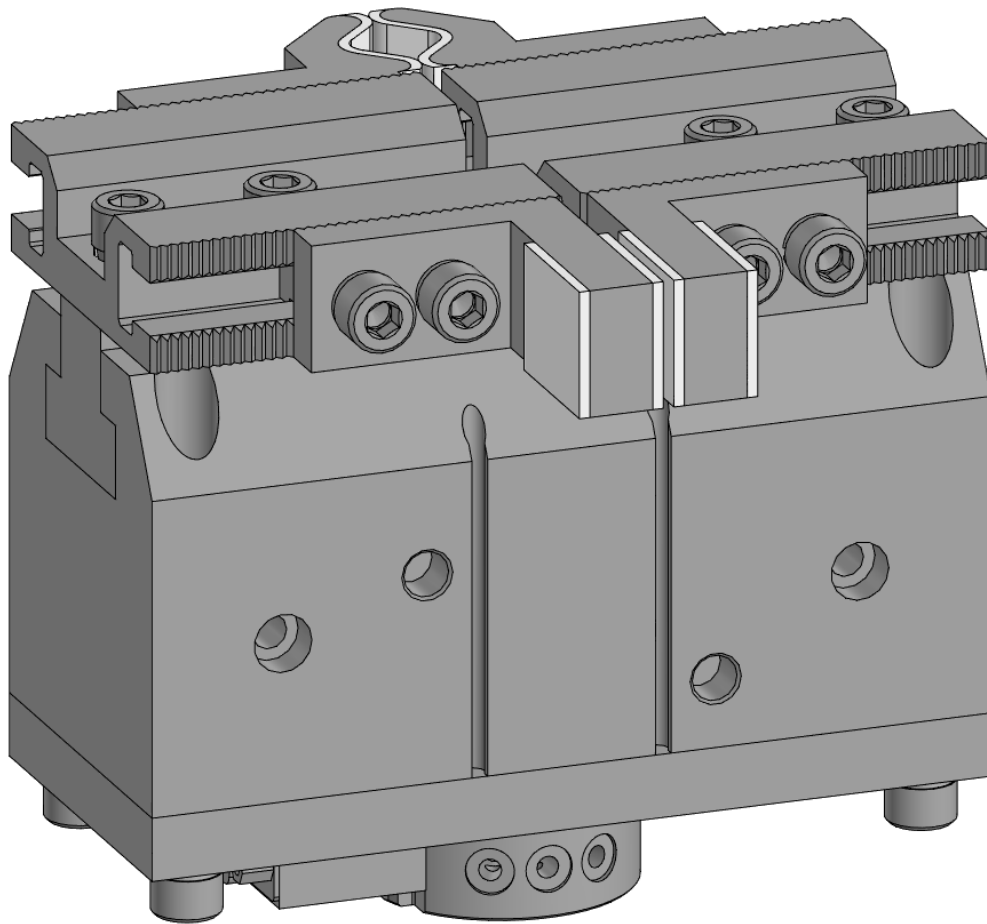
Захоплювальний пристрій для деталей типу вилки
